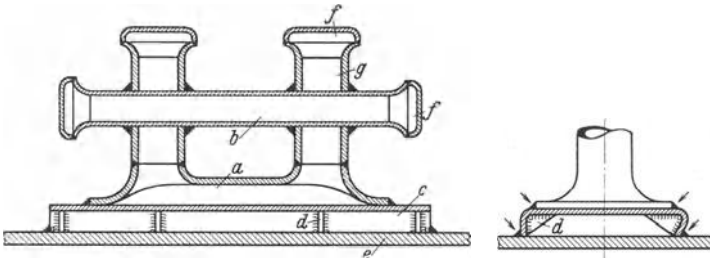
Geschweißter Stahldoppelpoller.
